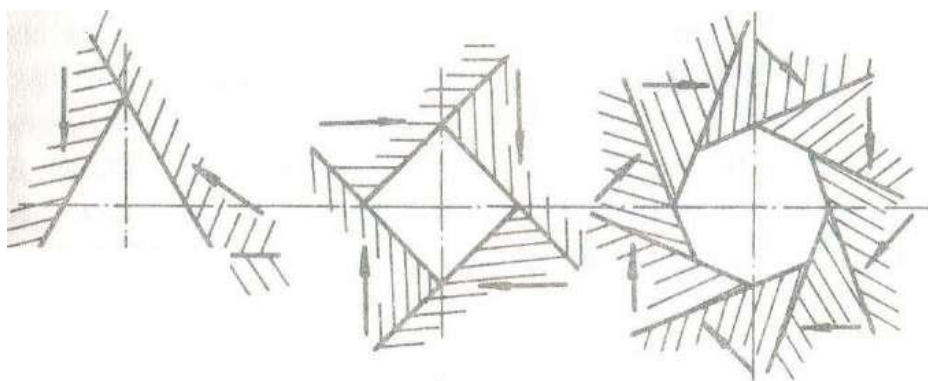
Варианты схемы сопряжения бойков РОМ прессовой установки.
